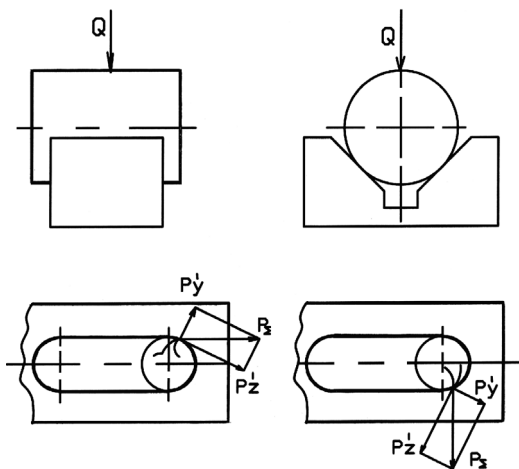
Действие сил резания на заготовку при фрезеровании шпоночной фрезой
